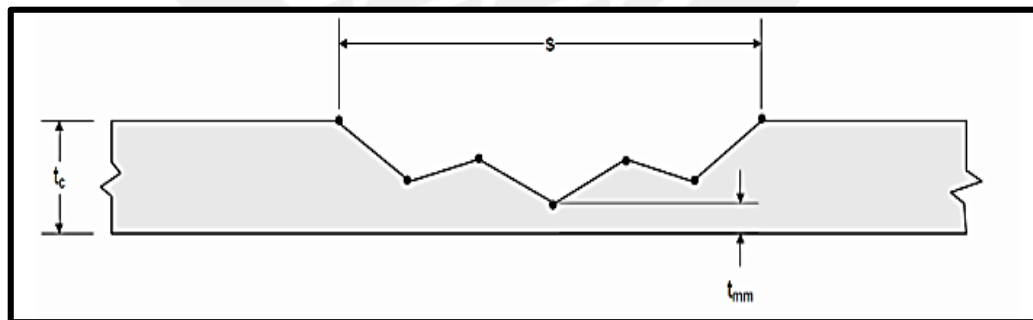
Corte longitudinal de zona con daño<sup>12</sup>
